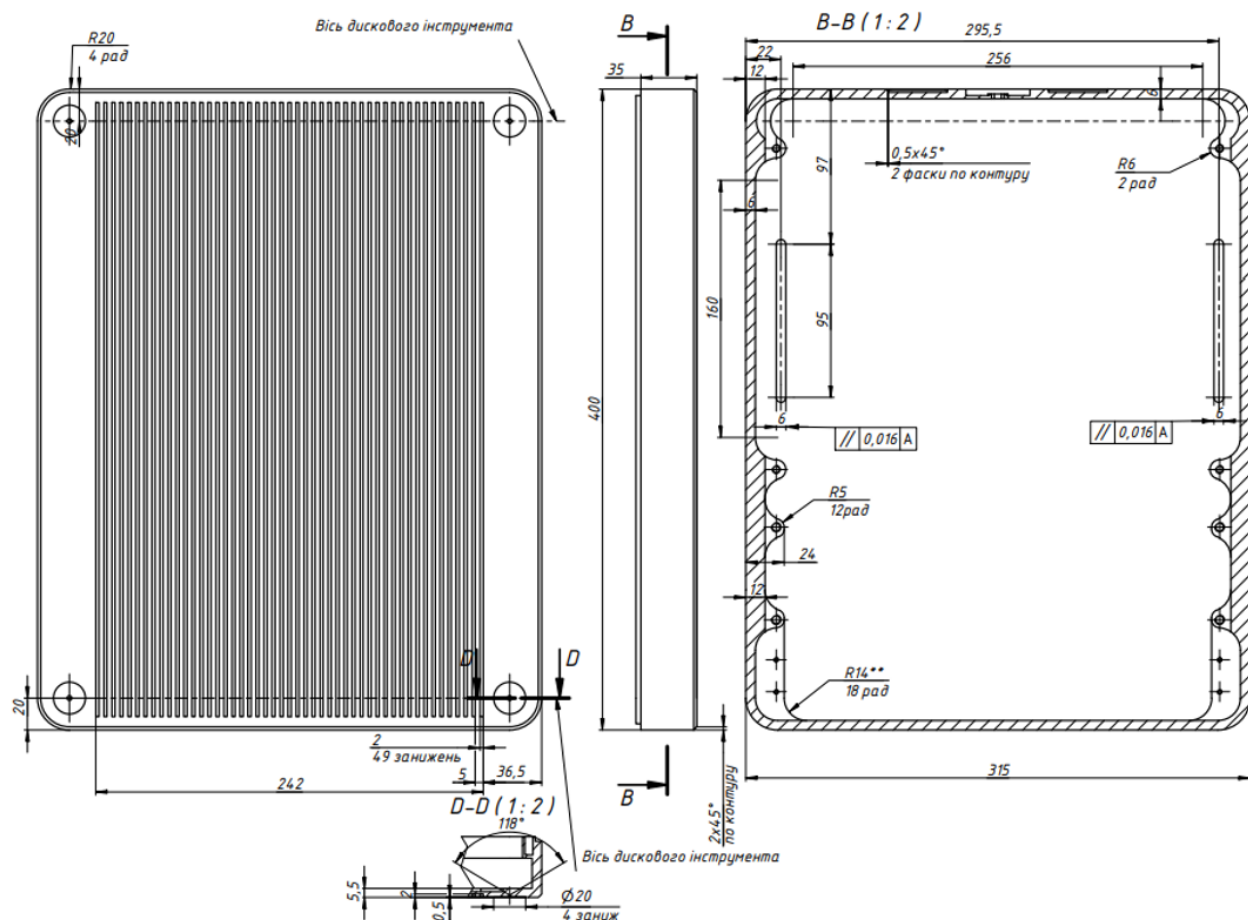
Фрагмент креслення деталі АЛНА.741532.022 Основа корпусу
